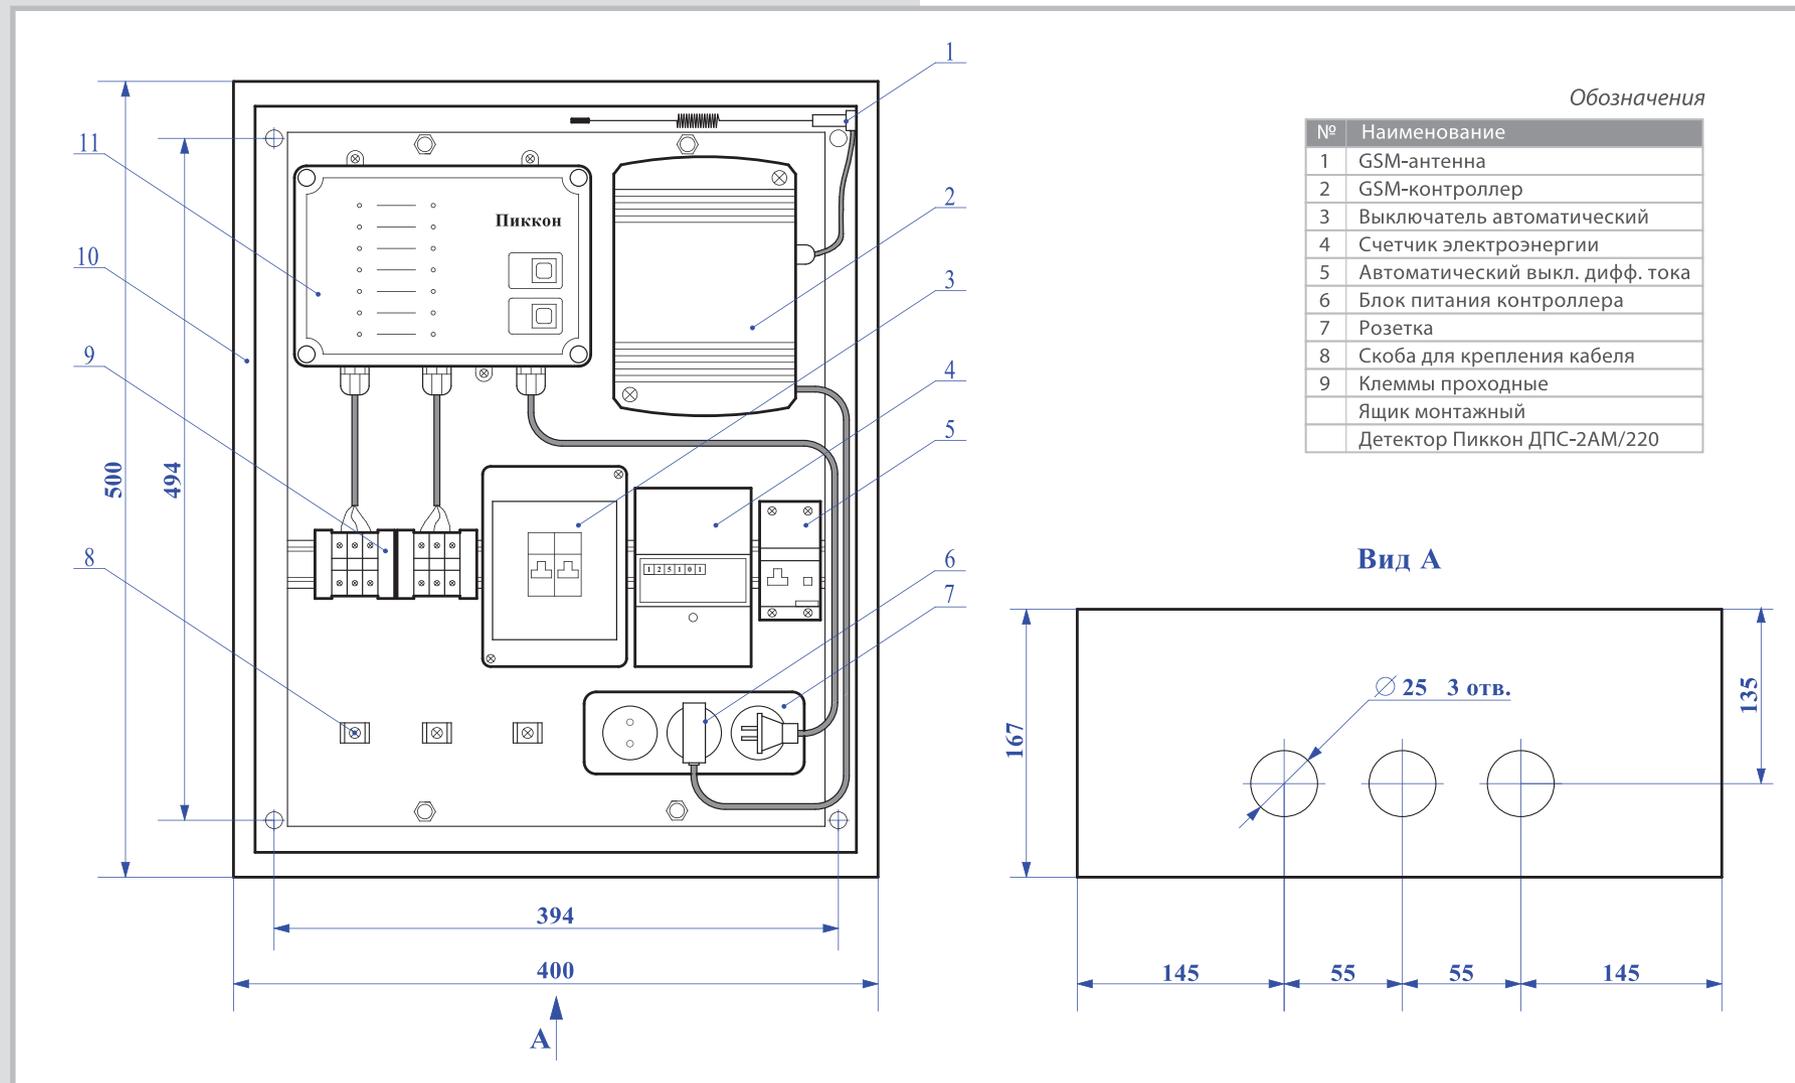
Габаритный чертеж комплекта оборудования ДПС-GSM.220/ТВ
